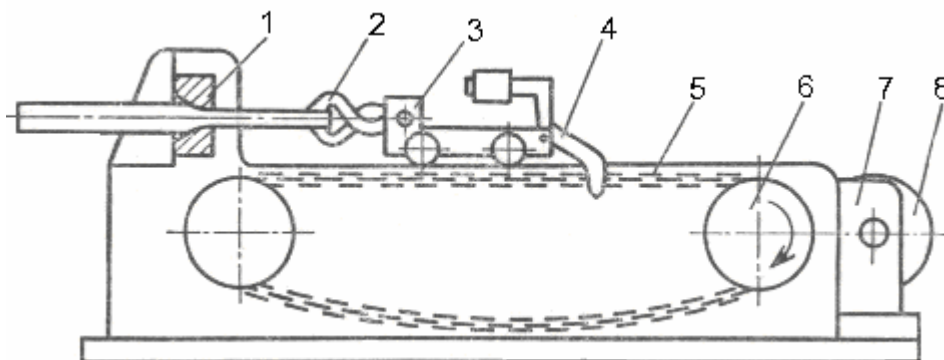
Цепной волочильный стан: 1 – волока; 2 – клещи; 3 – каретка; 4 – тяговый крюк; 5 – цепь; 6 – ведущая звездочка; 7 – редуктор; 8 – электродвигатель
